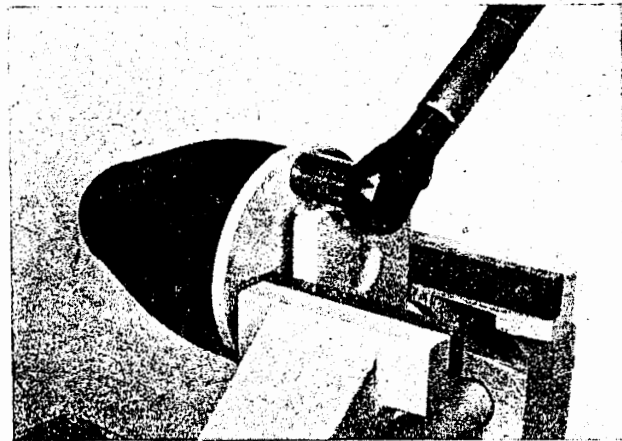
Gummifeder mit Druckstück verschrauben – Anzugsmoment
